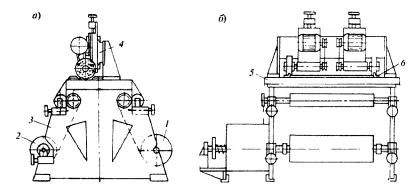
Общий вид станка модели ЗШ для зачистки кромок шлифшкурки: a- вид сбоку; b- вид спереди;
